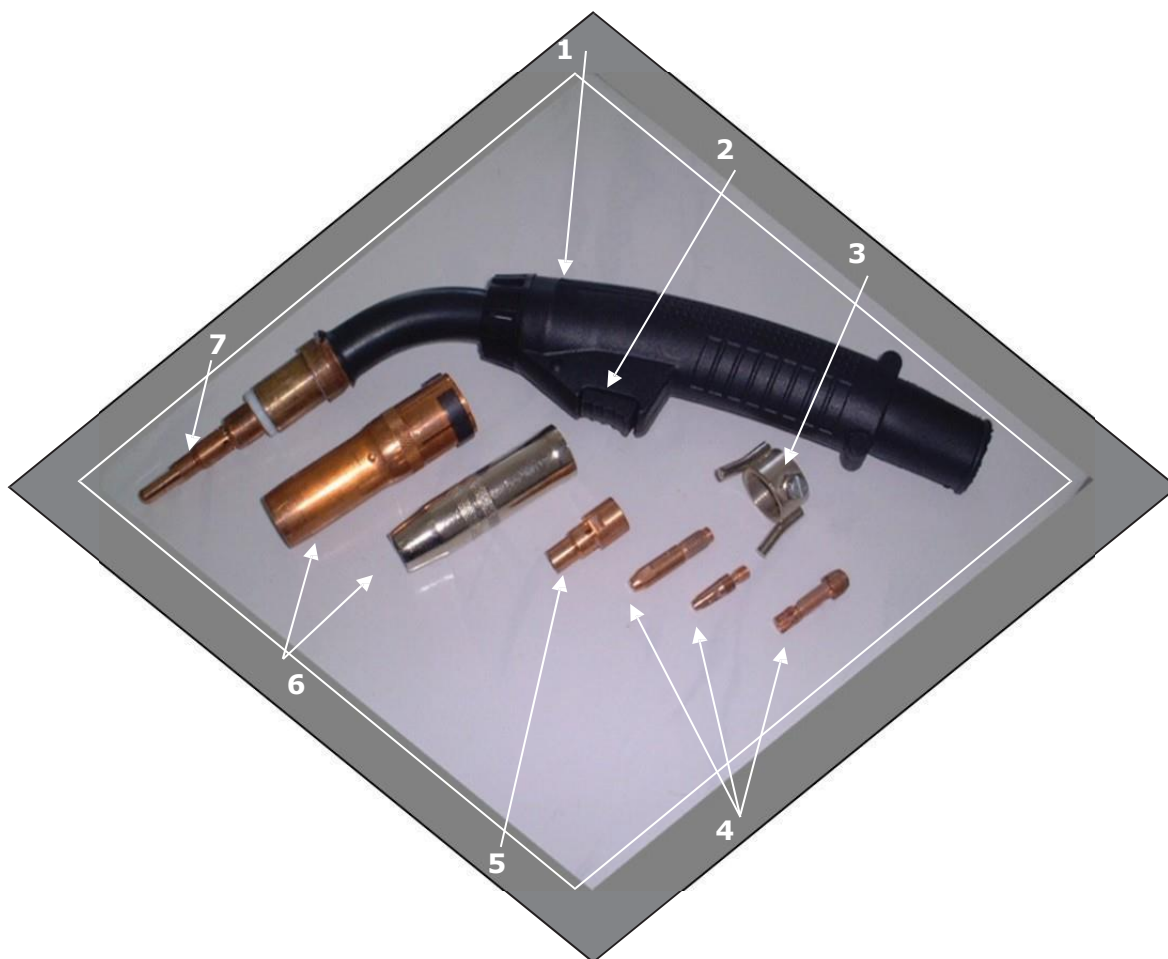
Cuerpo de la pistola; 2 Interruptor de encendido/apagado o de enclavamiento; 3 Fijación del espaciador de soldadura por puntos; 4 puntas de contacto; 5 Difusor de gas; 6 Cubiertas de gas; 7 Conjunto de la cabeza de la pistola (menos la cubierta). Fuente: TWI
